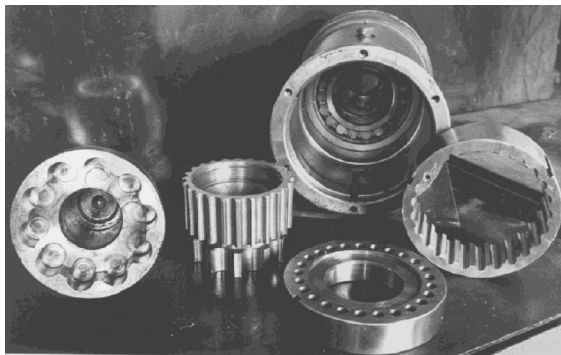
Опытный редуктор ПК-165 с промежуточными телами качения в разборе
